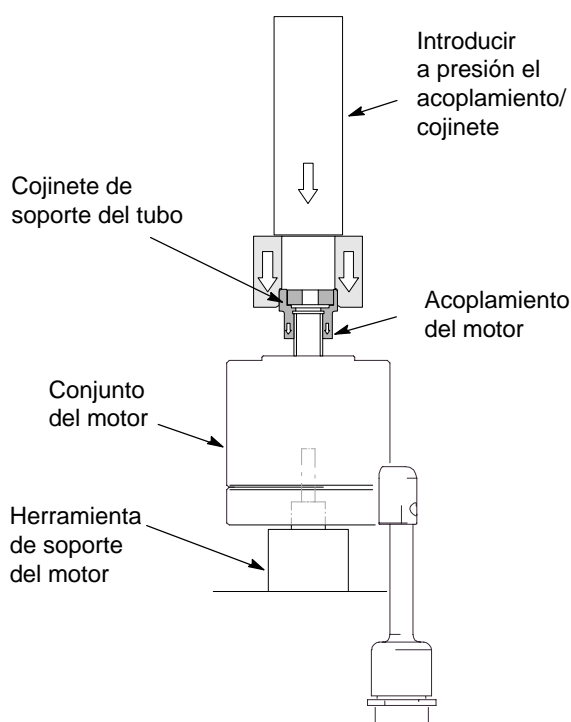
Montaje del cojinete de soporte del tubo T10658
